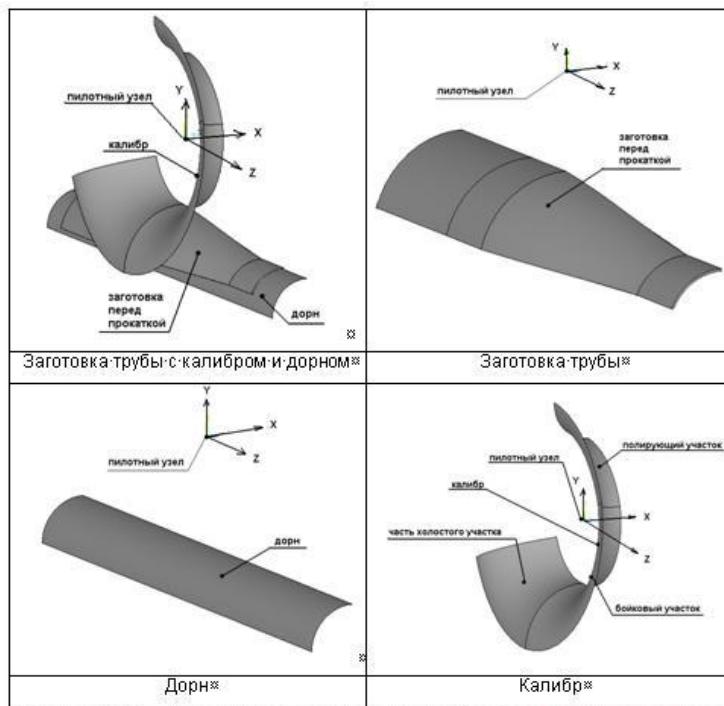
Расчетная модель прокатываемой трубы с калибром валка перед прокаткой
